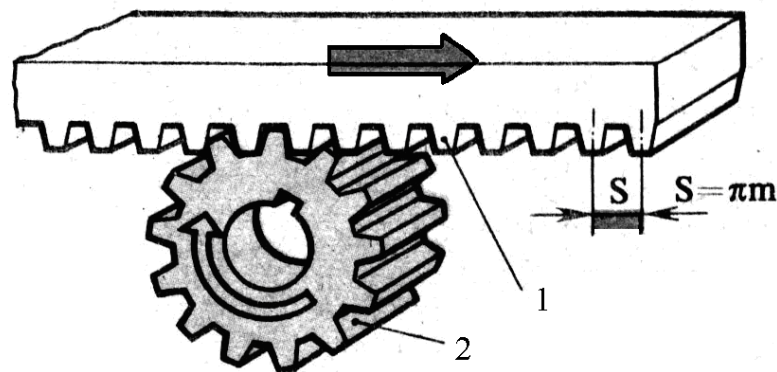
Рейкова пара: 1 – рейка, 2 – зубчасте колесо.
